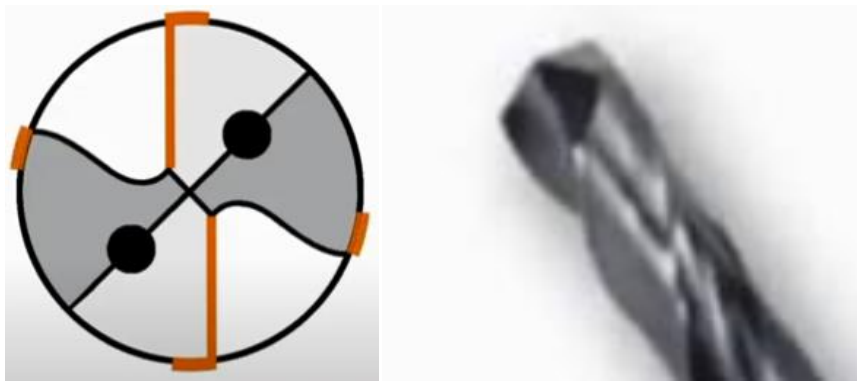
Схема розміщення чотирьох напрямних стрічок та різальна частина свердла
